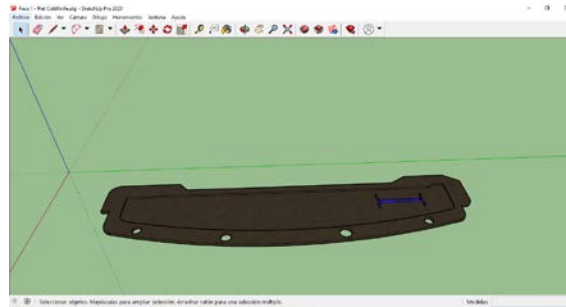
Sketch piel Upper con corte de Cold Knife
